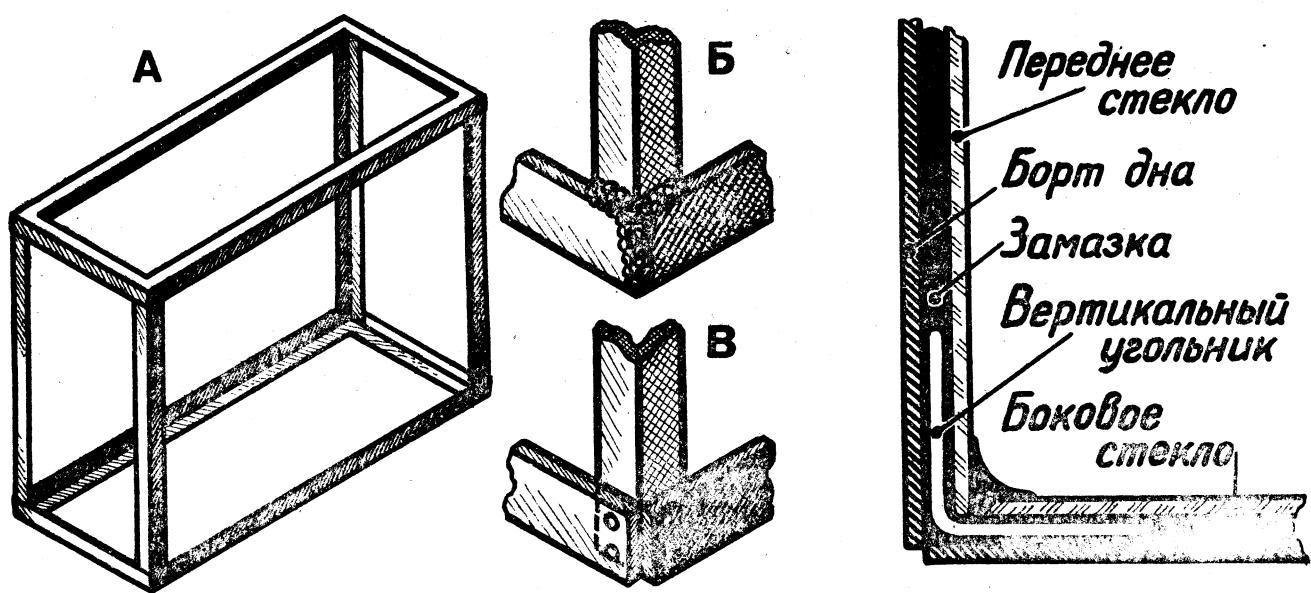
Каркас аквариума (А), соединение уголков сваркой (Б) и за-клепками (В)
